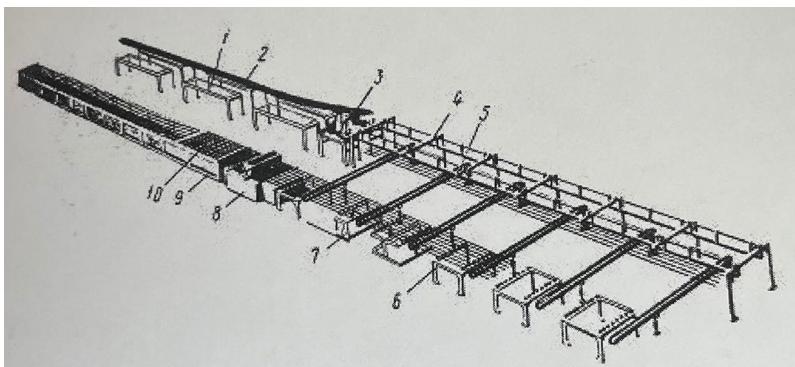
Общий вид линии 7850 для изготовления арматурных сеток шириной до 1450 мм: 1 – стеллаж СМЖ-491; 2 – пакет продольных стержней; 3 – механизмы СМЖ-485 выдачи стержней из пучка; 4 – приемно-выдающий лоток СМЖ-487; 5 – портал-раскладчик СМЖ-486; 6 – рольганги СМЖ-489; 7 – механизм СМЖ-488 подачи стержней; 8 – сварочная машина МТМ-35; 9 – пакетировщик СМЖ-490; 10 – сетка
